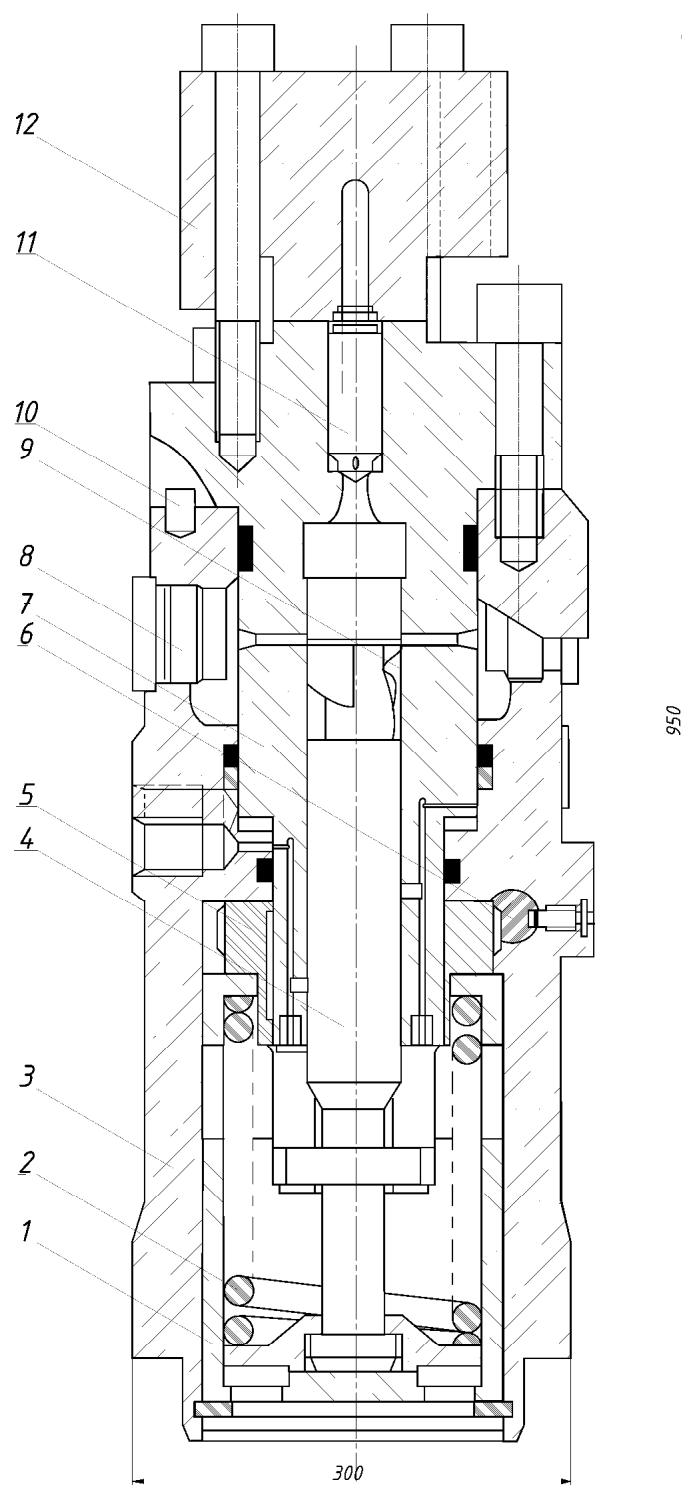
ПНВТ дизеля L28/32: 1 – штовхач; 2 – зворотна пружина штовхача; 3 – корпус; 4 – плунжер; 5 – зубчастий сектор; 6 – втулка; 7 – рейка; 8 – контрольні пробки з дифузійним компенсатором; 9 – відсічна кромка; 10 – установчий штифт; 11 – зворотний клапан; 12 – кришка
